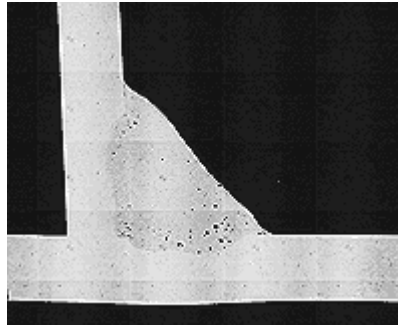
Porosidad en el material de soldadura
